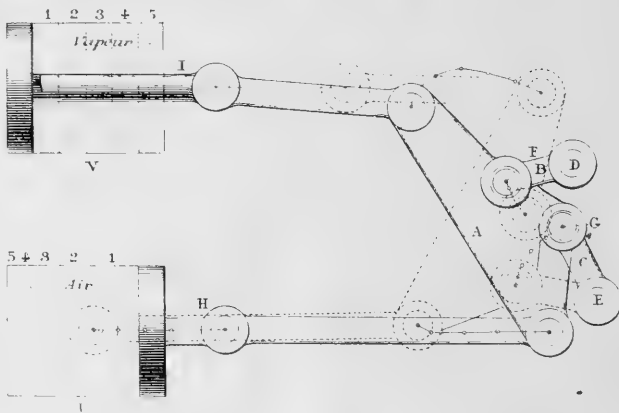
Représentation du mouvement combiné du piston à vapeur et du piston à air. — V , cylindre à vapeur; au-dessous, U , cylindre à air; I, tige du piston à vapeur; H, tige du piston à air; A, levier de manœuvre; D, E, points fixes; B, C, petites tiges reliant le levier A aux points fixes D, E; F, G, points où les tiges B, C, s'articulent au levier A. — A droite de la figure, le dessin en traits pleins représente une position extrême du piston; le dessin en traits tirés, la position contraire. — Les lignes verticales dans les deux cylindres séparent des déplacements correspondants de leurs pistons, déplacements numérotés de 1 à 5.
